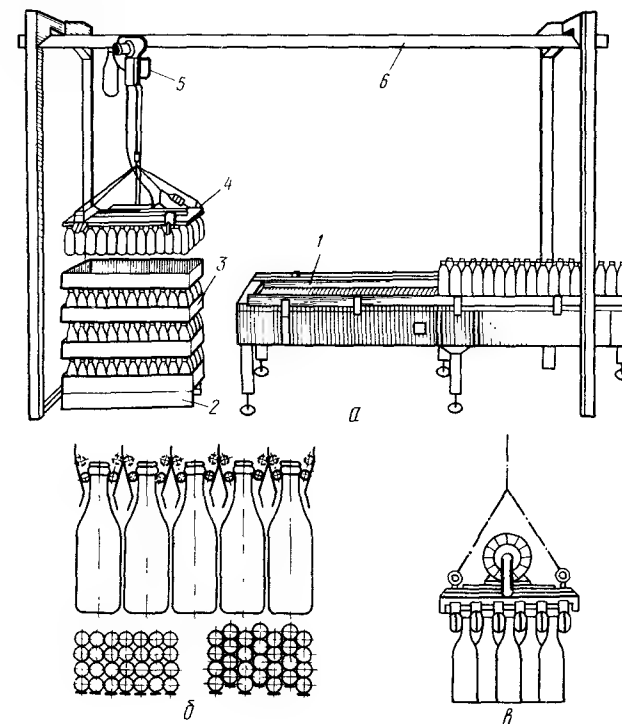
Установка для сборки и разборки пакетов-поддонов (а), устройства для захвата бутылок колодочными зажимами (б) и надувными рукавами (в):
